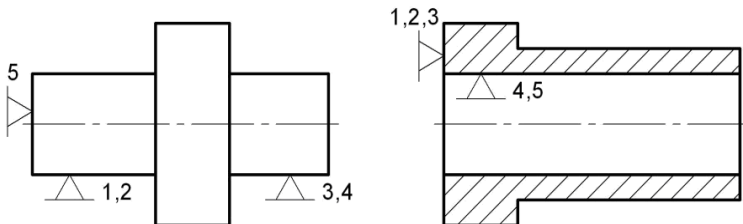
Схеми базування деталей типу тіл обертання:
